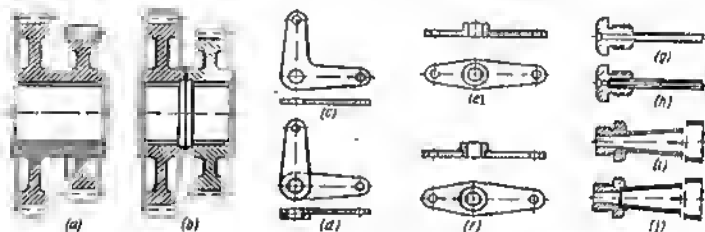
Simplificación del tratamiento mecánico aplicando construcciones soldadas
